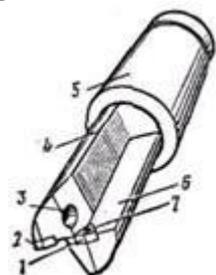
Сверло с поворотными неперетачиваемыми пластинками резания этим сверлом переходит в процесс точения, выполняемый двумя резцами, позволяя использовать рабочие качества и простоту современных токарных резцов. Форма пластинок и их
